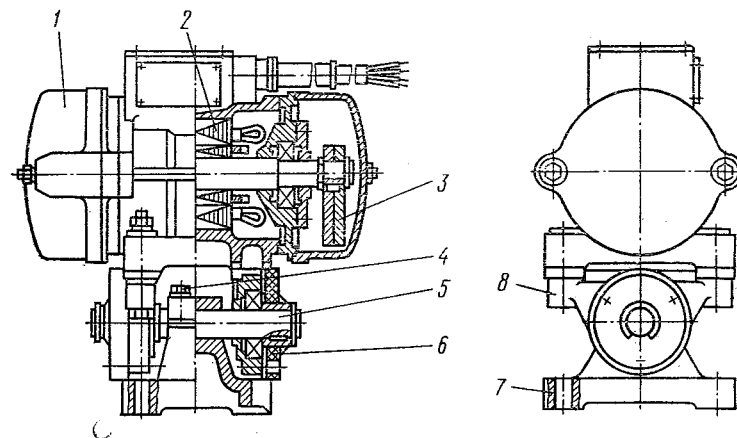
Вибратор ИВ-101 общего назначения с направленными колебаниями:
